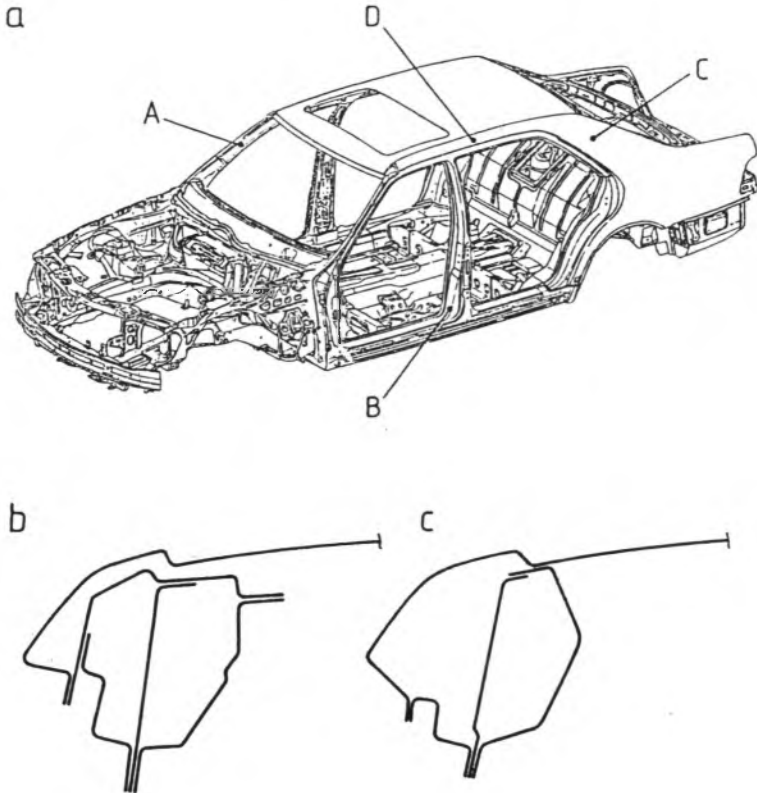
PKW-Dachlängsträger mit Dachblechanbindung in punktschweißgerechter (links) und laserschweißgerechter Ausführung (rechts)
